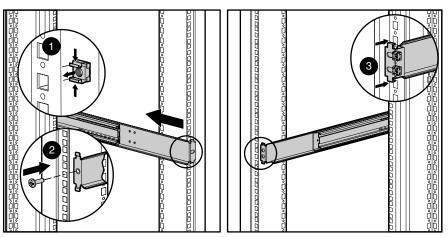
Instalando os trilhos de montagem na parte posterior e frontal do rack
